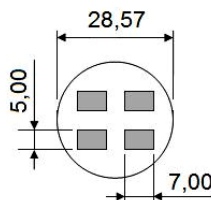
Perfil transversal do esquema de corte dos corpos para o ensaio de flexão.
